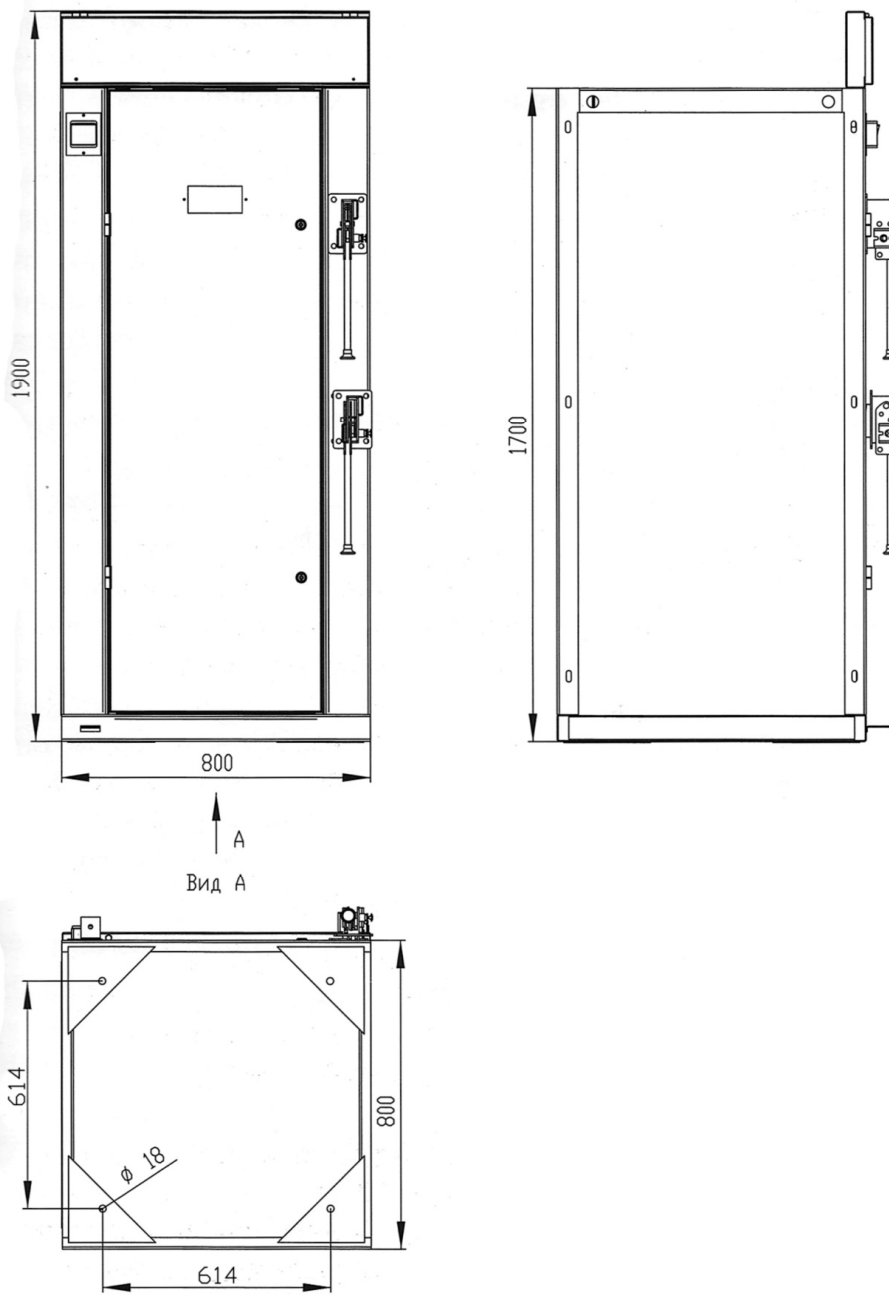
Внешний вид, габаритные размеры камер КСО393
